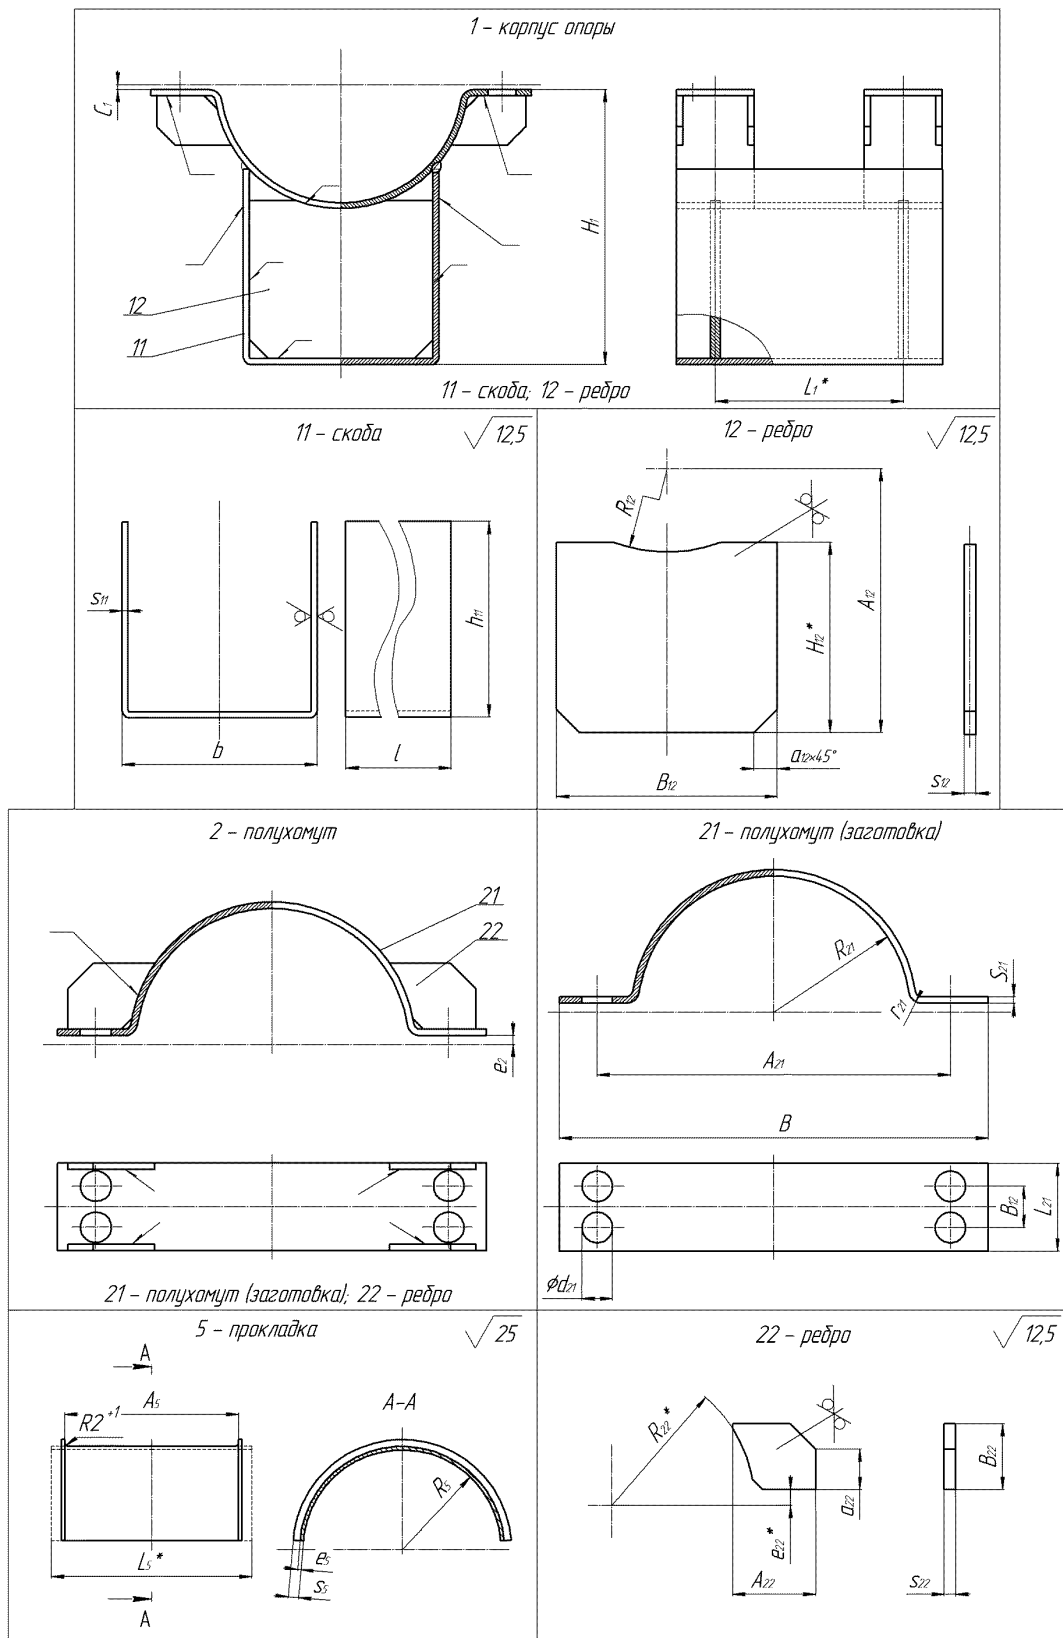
Детали изделий 01-XXXX-S-1C-02-A для  $D_H=1020 \div 1620$  мм
